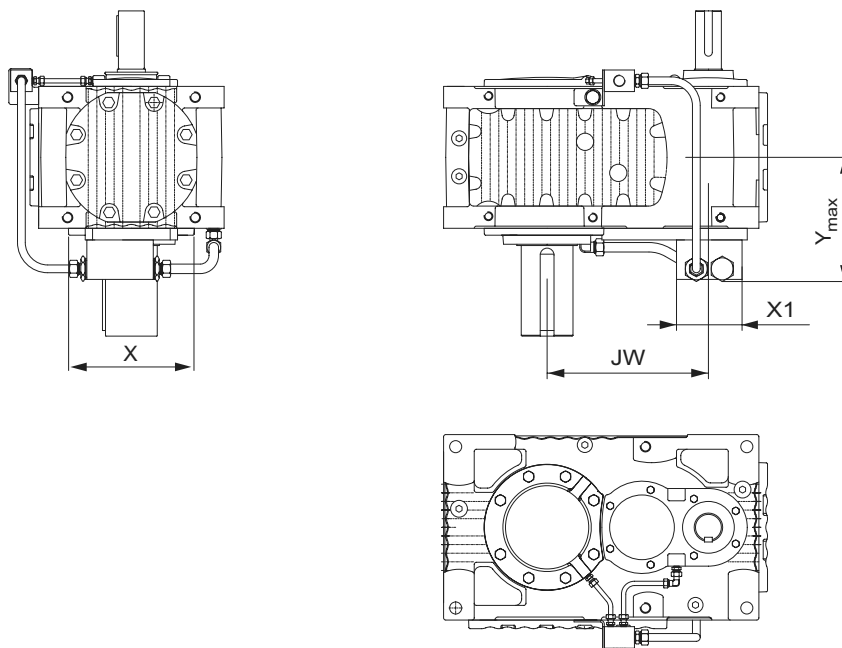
Dimensiones de montaje de MC2PV.. con bomba de extremo del eje 51843AXX
